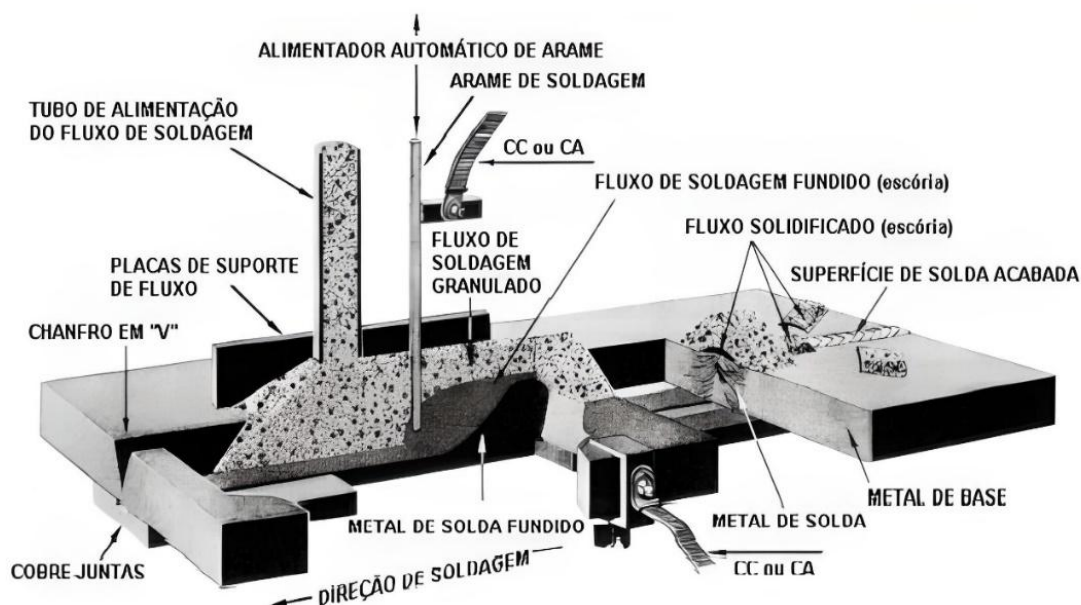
Representação do processo de soldagem por arco submerso, indicando os principais elementos presente no processo de soldagem. Fonte: Adaptado de [21].
